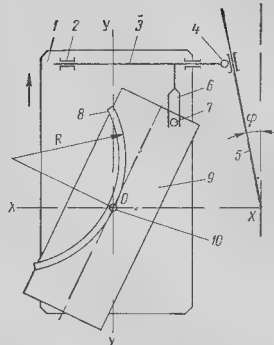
Кинематическая схема приспособления для строжки по радиусу
